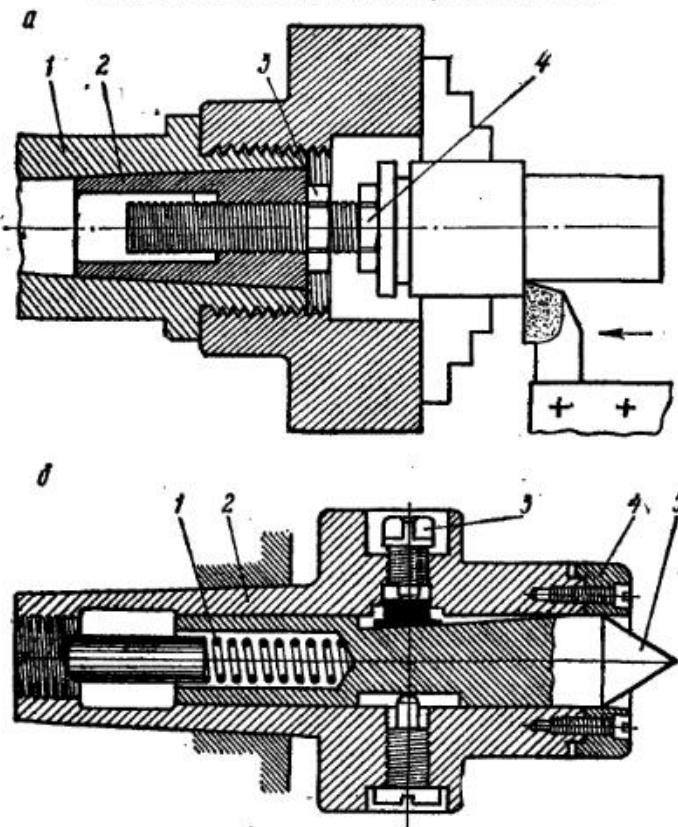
Шпиндельный упор (а) и упорно-плавающий центр (б)
